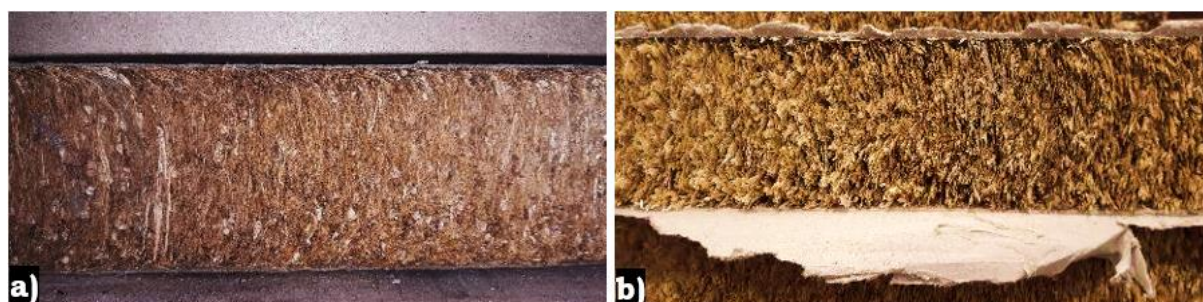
Panneau de paille a) avant usinage et b) après usinage.
